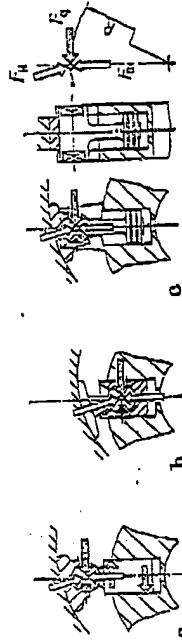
Kolbenbauarten als gegliedertes und integriertes Triebwerkteil mit Lageänderung des Gleitschub-Anlenkpunkts nach Weigle [123]. a, b Kolben mit Führung integriert (Druckkolben); c Kolben (Scheibenkolben) mit Kreuzkopfführung
